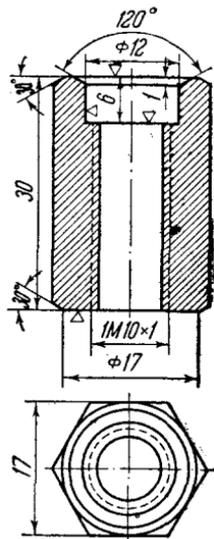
Дет. № 16-43. Гайка стяжной трубки распылителя
